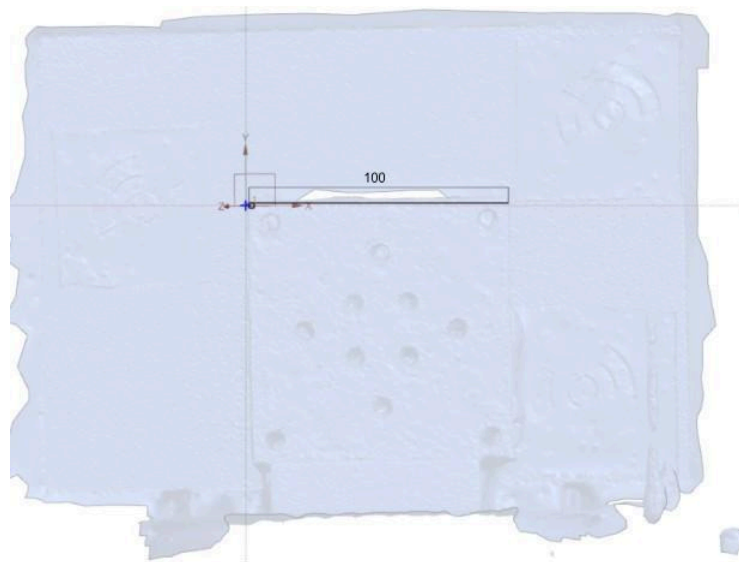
Inspeção dimensional preliminar no Siemens NX
